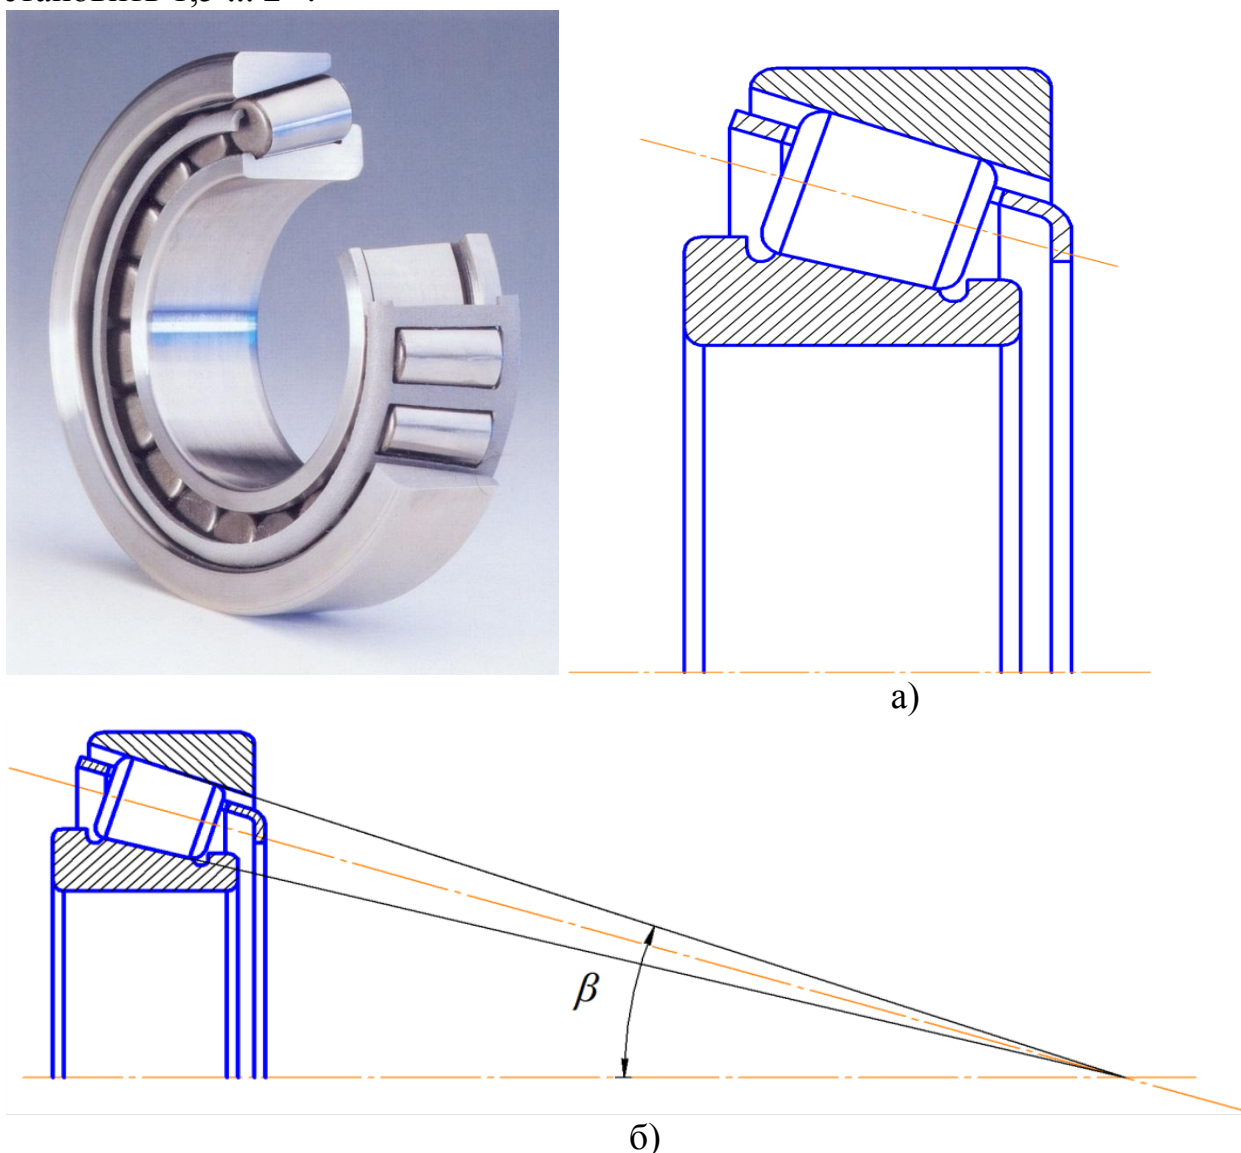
Конструкція роликового радіально-упорного конічного підшипника
